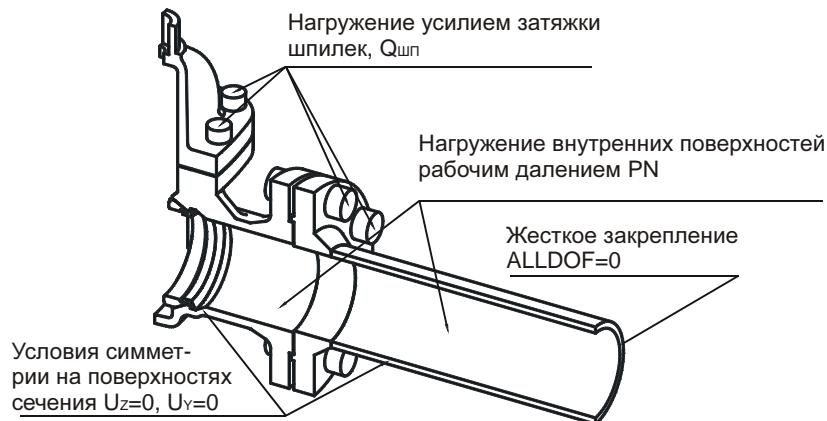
Расчетная схема для определения НДС корпусных деталей задвижки при нагружении монтажными нагрузками
